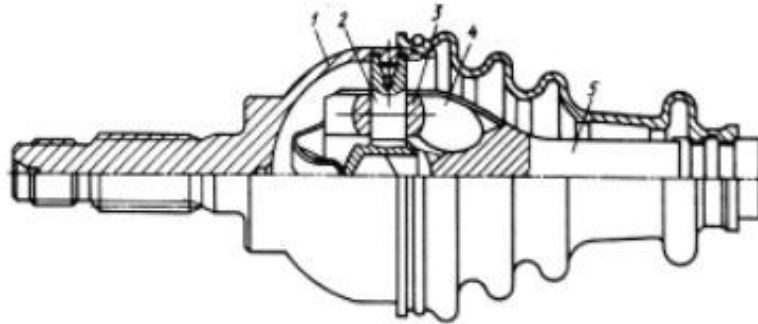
Трехшиповой жесткий карданный шарнир типа “трипод”: 1 – корпус; 2 – шипы; 3 – ролик с шаровой поверхностью; 4 – вилка; 5 – вал
